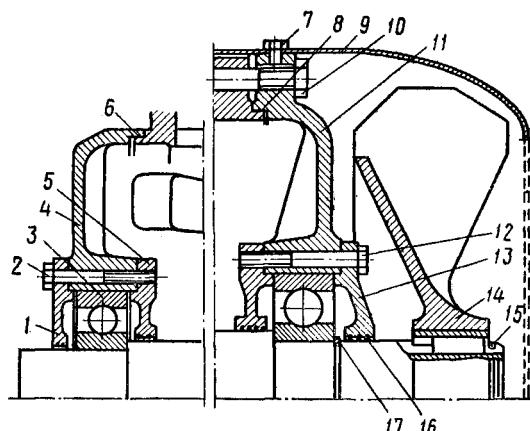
Конструкция подшипникового узла, смазка которого пополняется при разборке
